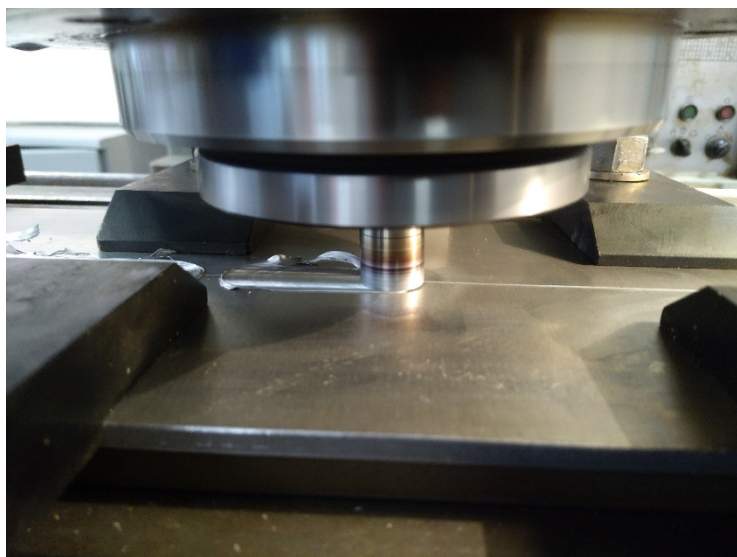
Процесс сварки трением с перемешиванием
